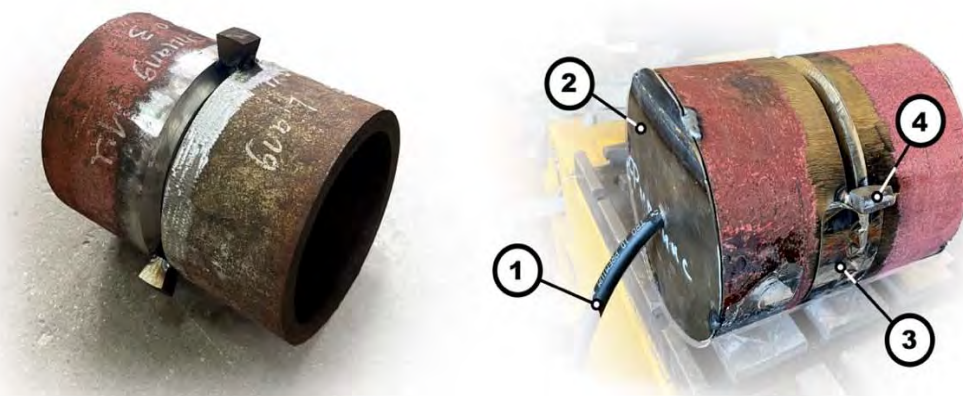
Внешний вид подготовленного под сварку и сваренного стыкового соединения труб:
